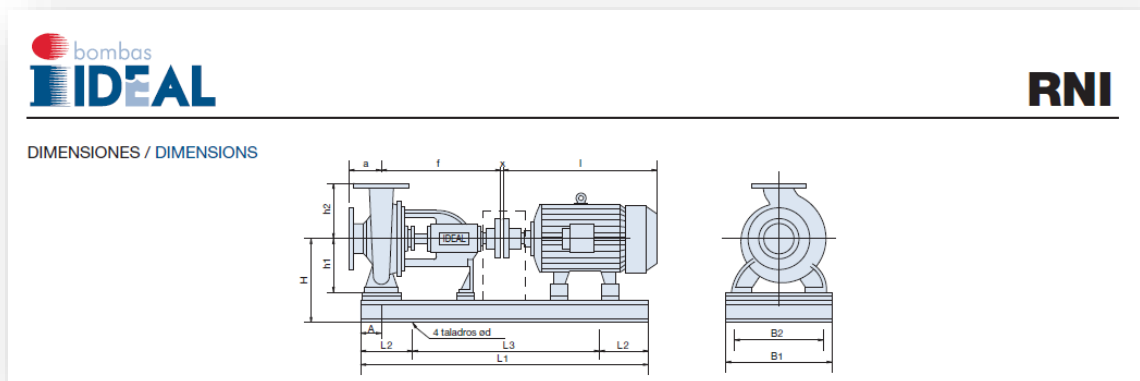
Cota de dimensiones con bancada (bomba + motor)
